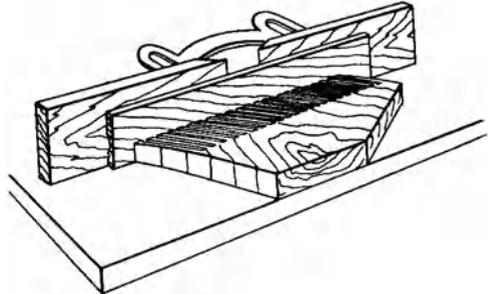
Druckvorrichtung und Rückschlagsicherung für Arbeiten an der Fräsmaschine.
